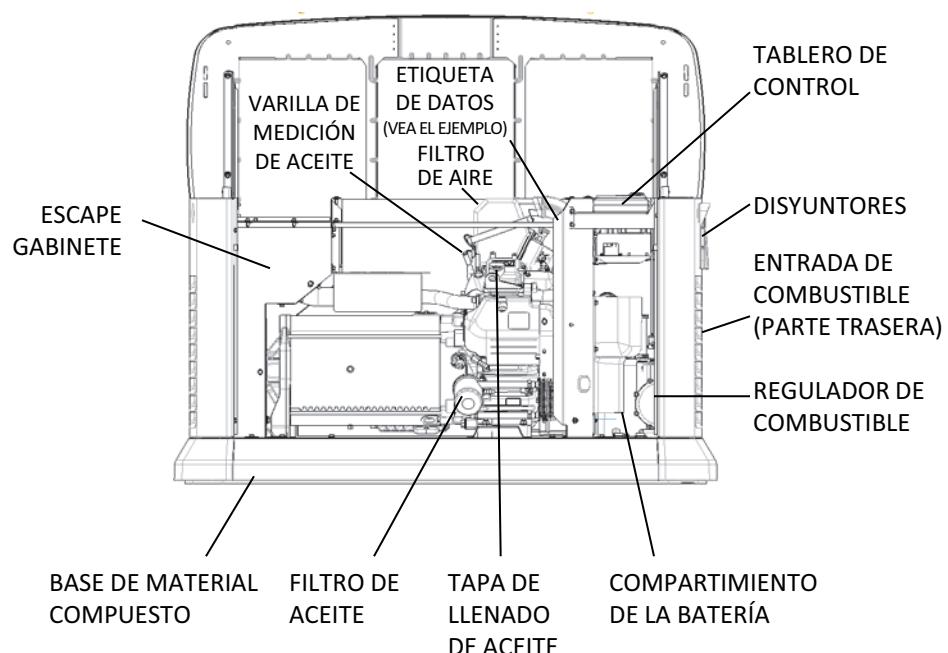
Unidad de 10 y 13 kVA, motor GT-990
